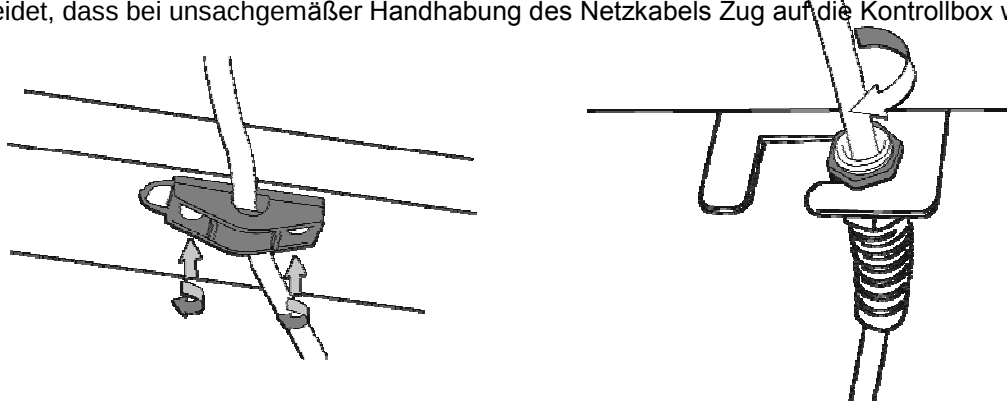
Befestigung der Zugentlastung (beide Typen)
